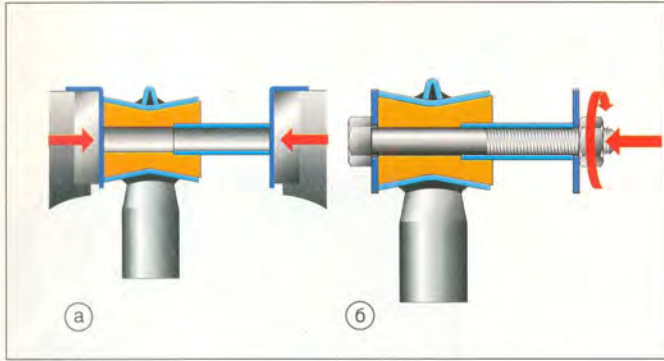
Запрессовка стальной втулки: а – в тисках; б – с помощью болта.
